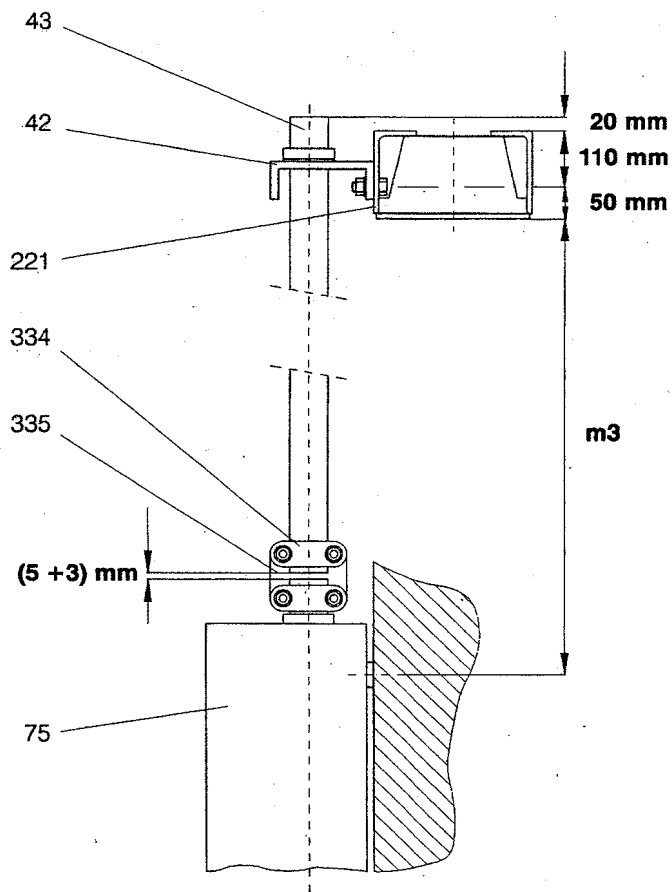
Установка приводного механизма разъединителя; отдельный монтаж при размере $m3$ меньше 6 м. Монтажные размеры
